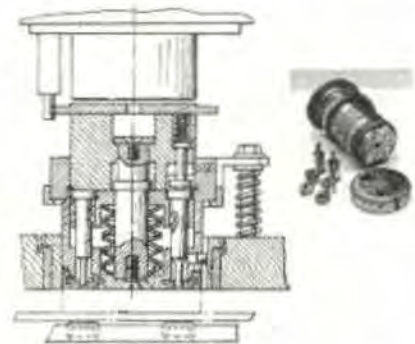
Accionamiento de una herramienta Multitool de Strippit Inc. y herramienta multitool de Mate Punch & Die Co.
